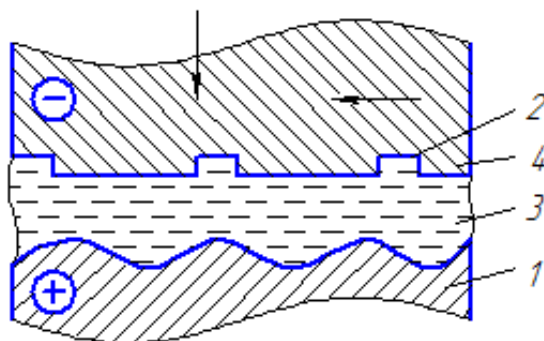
Схема анодно-механической обработки: 1 – инструмент (катод); 2 – пазы, способствующие удалению продуктов эрозии из зоны обработки; 3 – рабочая среда; 4 – заготовка
